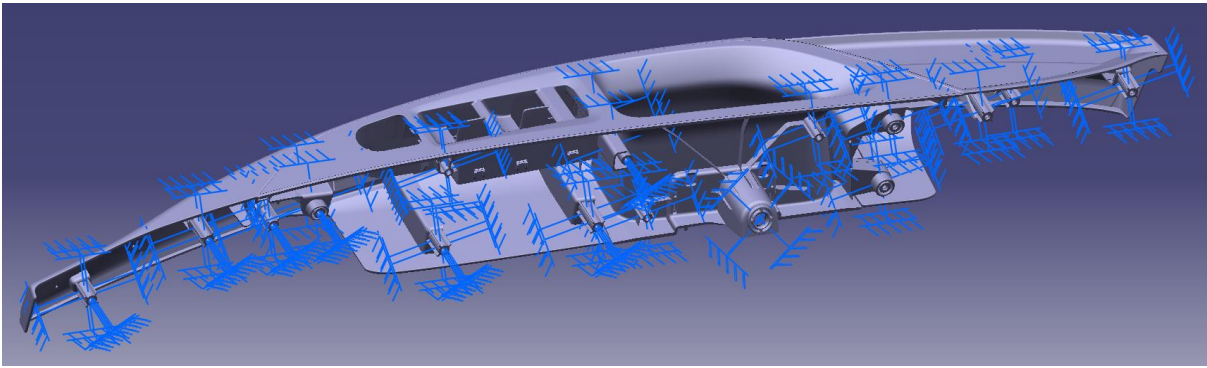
Restricciones en torretas de atornillado (vista posterior)
